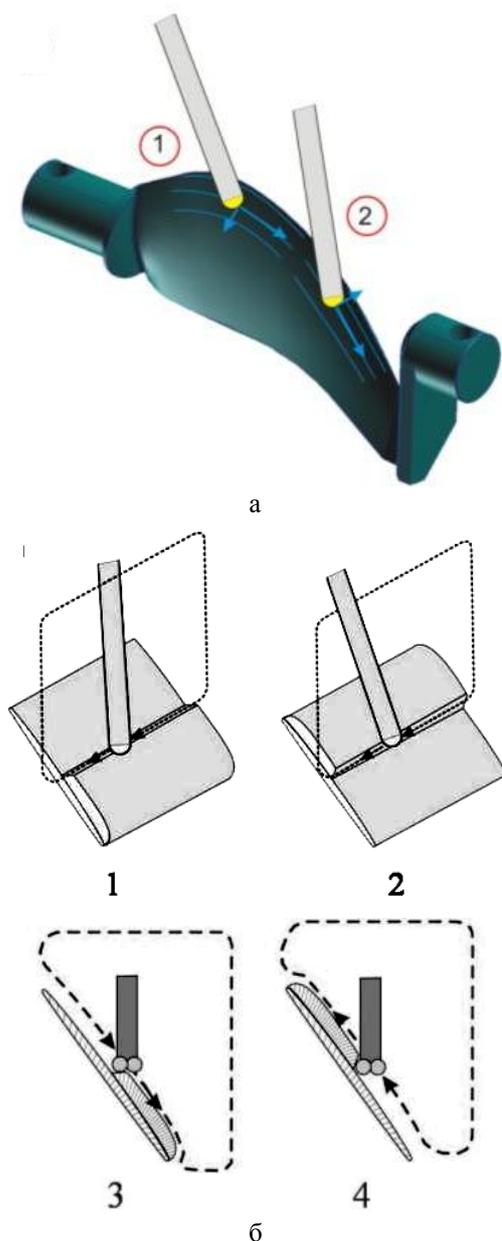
Варианты движения фрезы при обработке лопатки ГТД: а – схема закрепления; б – траектории
